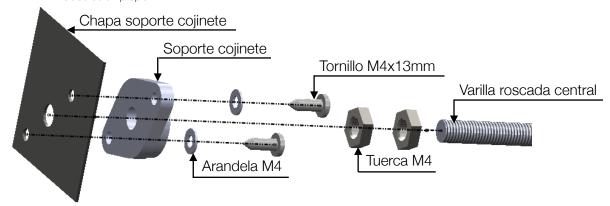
Detalle fijación varilla central a las chapas soldadas. Fuente: elaboración propia.
